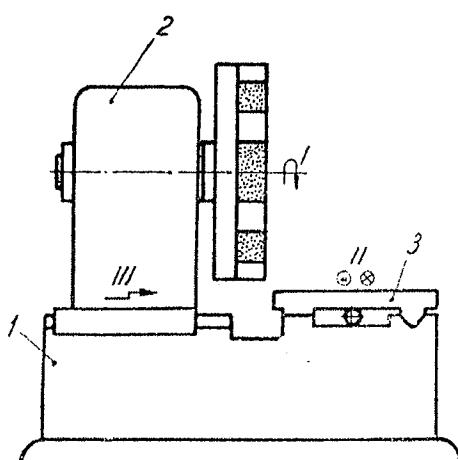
Mașină de rectificat plan orizontală cu masă dreptunghiulară și abrazare frontală: 1 – batiu; 2 – montant; 3 – masă
